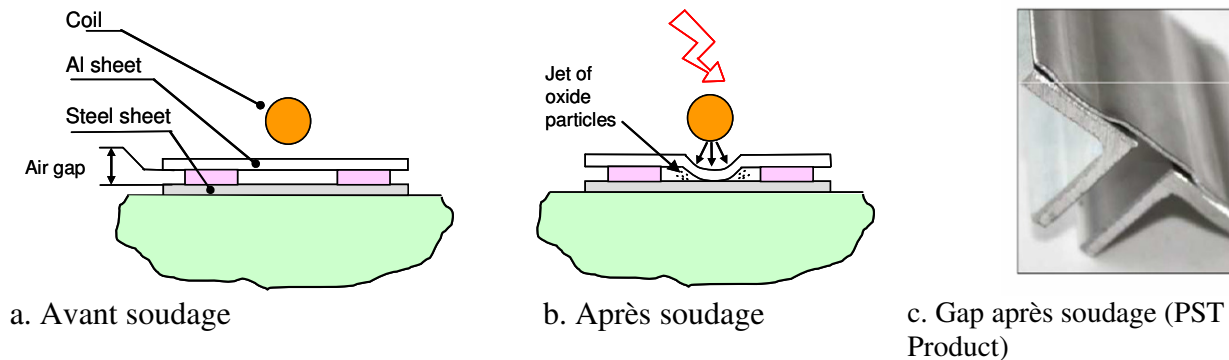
Principe du Linear Magnetic Pulse Welding.
